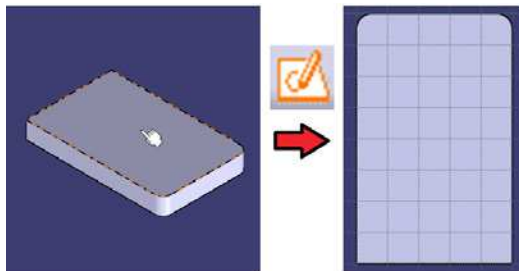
Bauteiloberfläche als Stützelement für eine neue Sketch
